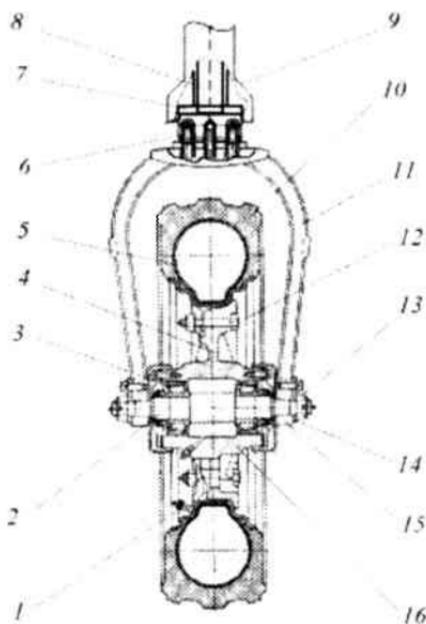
Передний мост хлопководческого 3-колесного трактора: 1 – вентиль, 2 – ось; 3 – роликовый подшипник; 4 – диск; 5 – камера; 6 – шпилька; 7 – специально-упорный шариковый подшипник; 8 – вертикальный поворотный вал; 9 – цилиндрический кронштейн; 10 – покрывка; 11 – вилка; 12 – обод; 13 – гайка; 14 – планка - замок; 15 – паза; 16 – ступица
